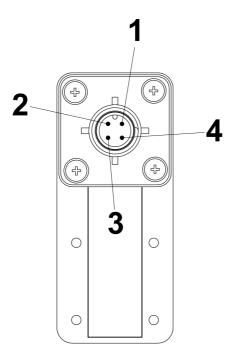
Pin-Belegung Gerätestecker M12x1 (Form 30x70)
